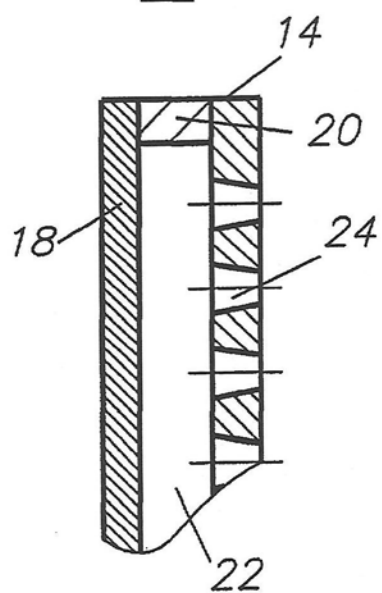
Поперечный разрез корпуса мельницы у места его соединения с загрузочным устройством.
